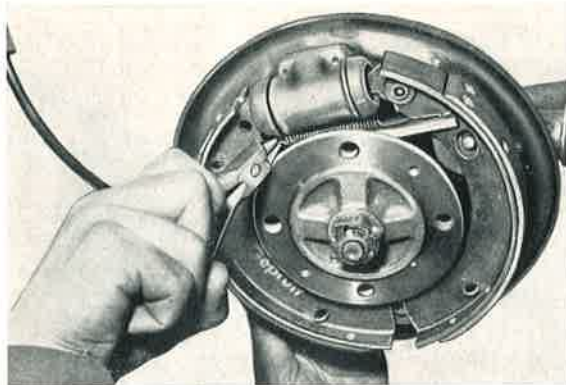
/2: Während man mit Hilfe einer spitzen Flachzange die Zugfeder genügend auszieht, wird mit der anderen Hand mittels eines kleinen Schraubenziehers die Federöse von hinten in das Aufnahme Loch gedrückt.
